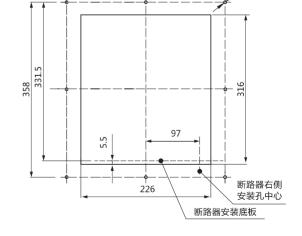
ZMW50-200A~1000A抽屉式断路器 Figure 3: Draw-out type circuit breakers dimensions
